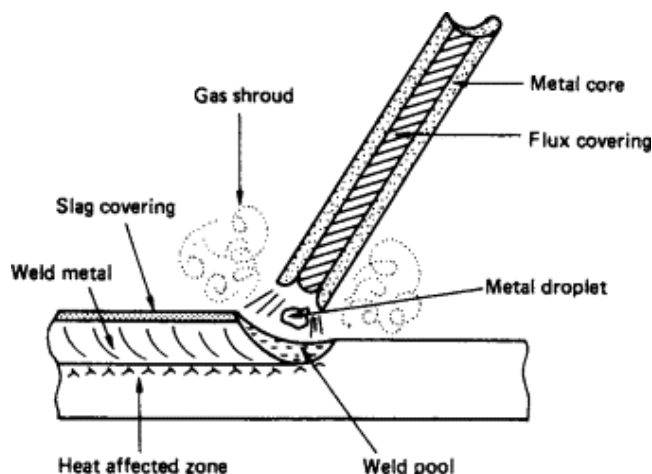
Схема сварки порошковой самозащитной проволокой
